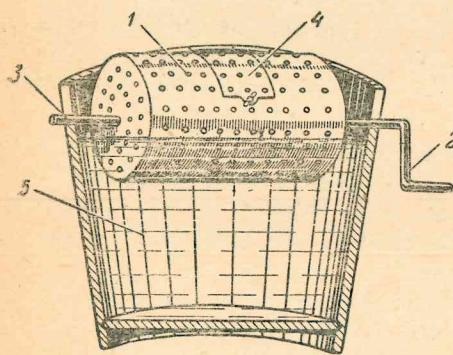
Приспособление для промывки колец Рашига, вынутых из тонкого очистителя газа:
